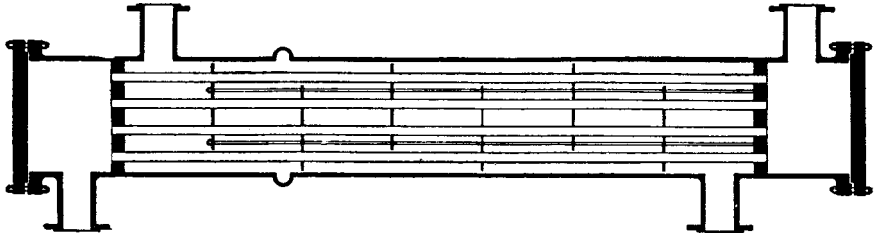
Intercambiador con cabezal de tubos fijo con carretes integrales. (Patterson Foundry & Machine Co.)
